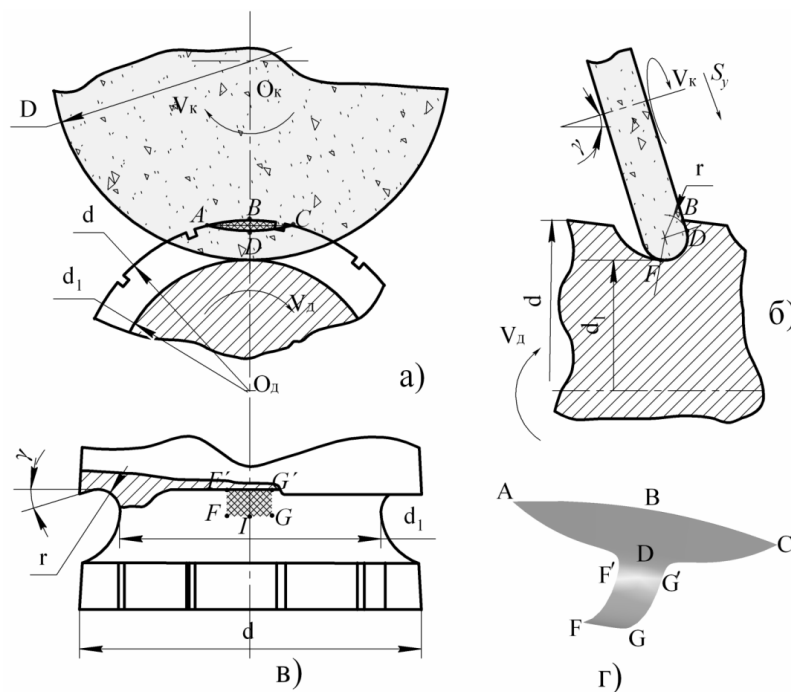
Схема контактирования поверхности круга с заготовкой: а,б - боковой поверхности; в - периферийной поверхности; г - суммарная поверхность контакта
